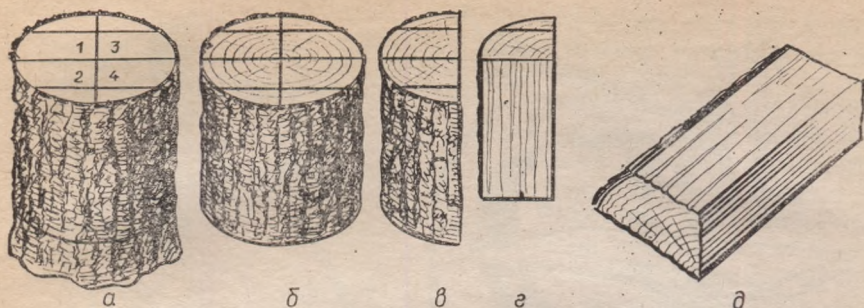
Схема раскладывания чурака на заготовки для топорика:
